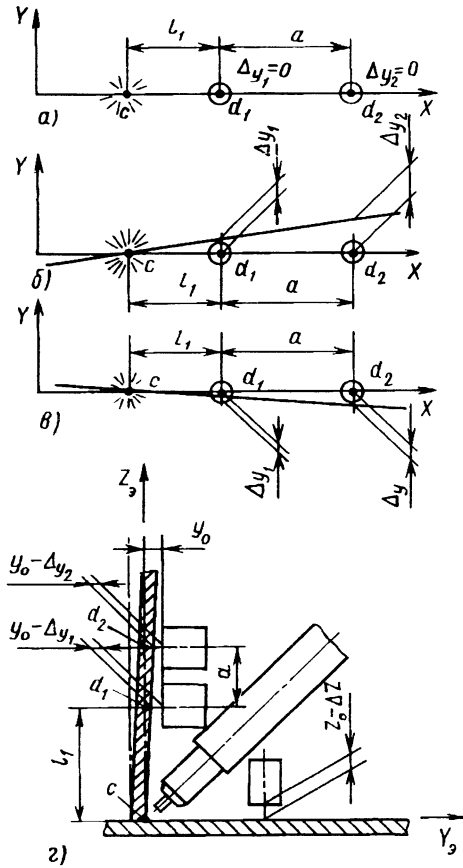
Метод линейной экстраполяции с использованием двух датчиков, расположенных впереди точки сварки (а—в) и сбоку от точки сварки (г) (d_1, d_2 — точки измерения; c — точка сварки)
